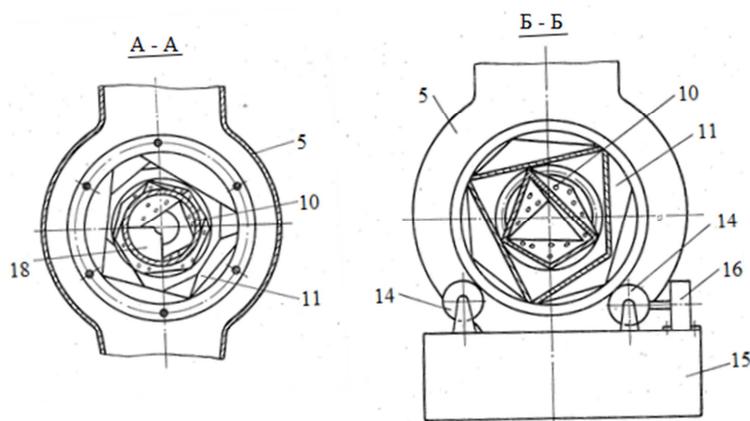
Разрезы А–А и Б–Б на рисунке 2 (5-кожух, 10- внутренний винтовой барабан, 11-наружный винтовой барабан, 14-четыре опорных катка, 15-рама, 16-привод 18-двухступенчатая винтовая навивка)
